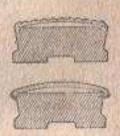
Грузовые плоцадки лыж, обитые режной с воздушными подушнами
